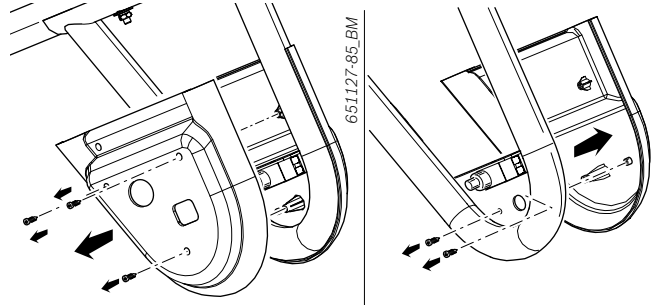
Abdeckung des Sonar-Messfühlers entfernen
